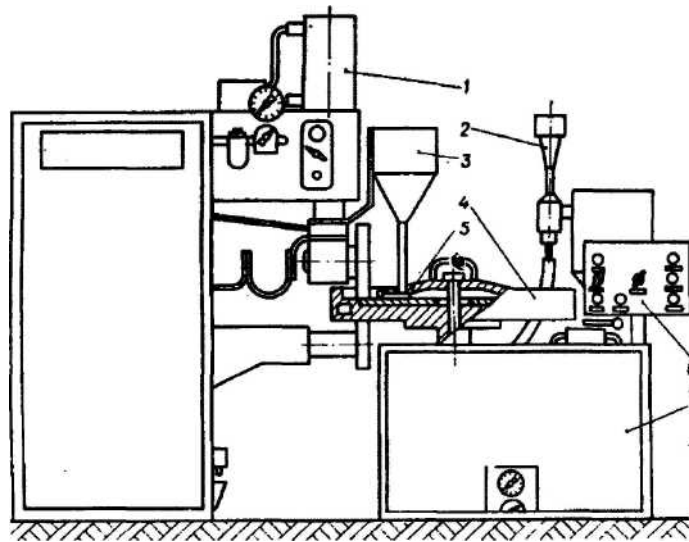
Схема установки для електроконтактного наплавлення дискових ножів [17]:
